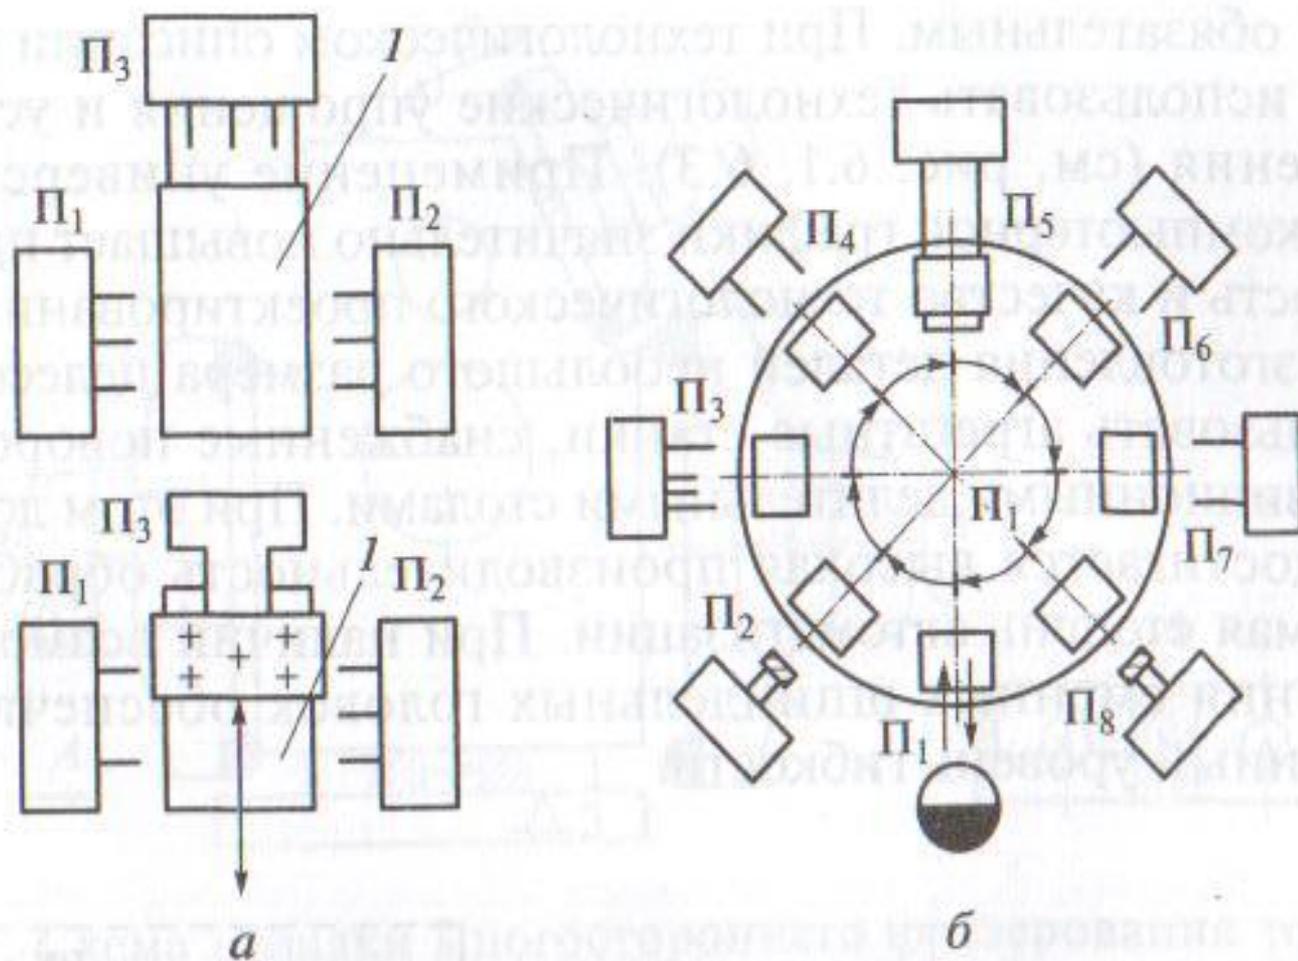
Схемы агрегатного станка (а) и агрегатного полуавтомата (б):
